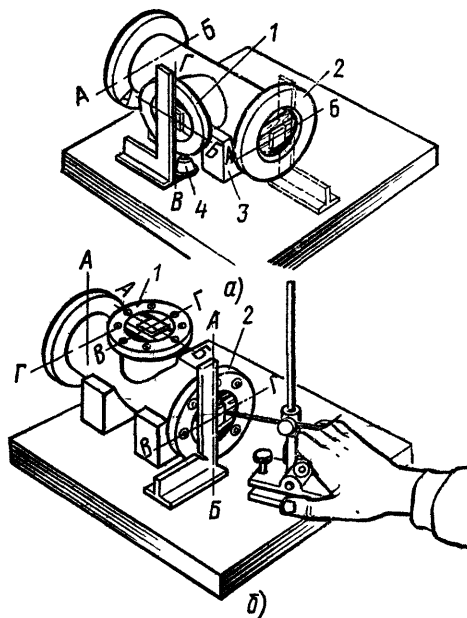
Разметка заготовок с перекаровкой: а — установка детали на призмы; б — нанесение разметочных рисок
